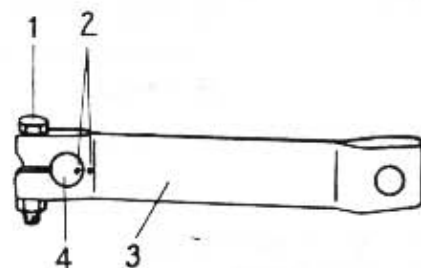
MONTAŻ ZEWNĘTRZNEJ TULEJKI ŁOŻYSKUJĄCEJ WAŁEK WYŁĄCZAJĄCY SPRZĘGŁO
